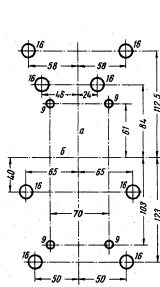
Сверление отверстий для установки на изоляционных плитах контакторов типа КТИ 522 и КТИ 542 с задним присоединением
